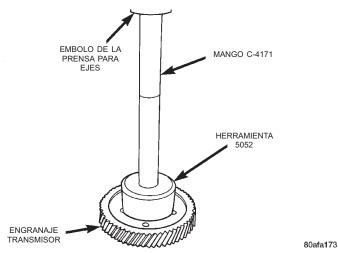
Instalación del cono de cojinete del engranaje transmisor
